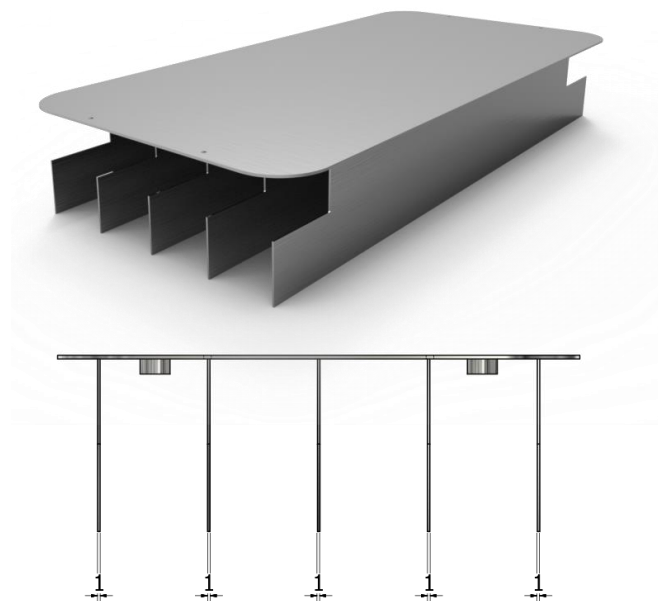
Detalles e isometría de la estructura de paredes de boleó
